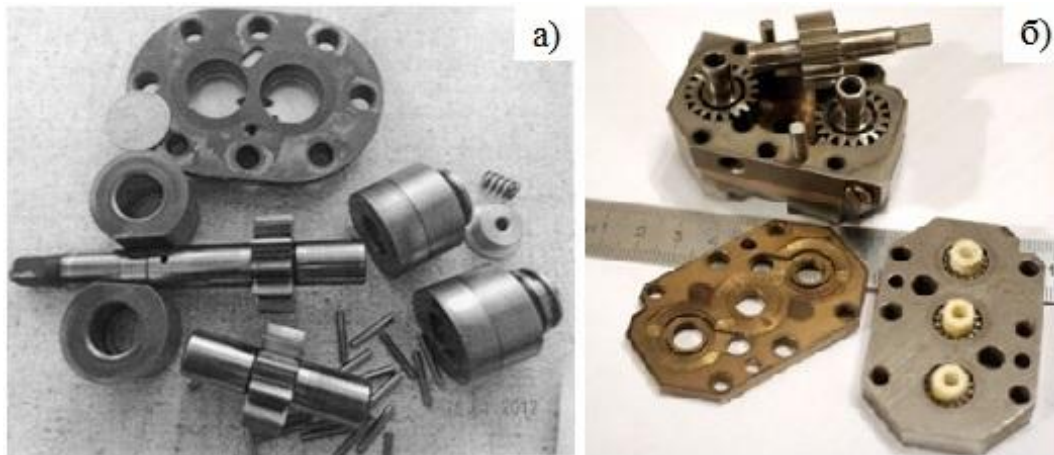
Детали шестеренных насосов с игольчатыми подшипниками опор
